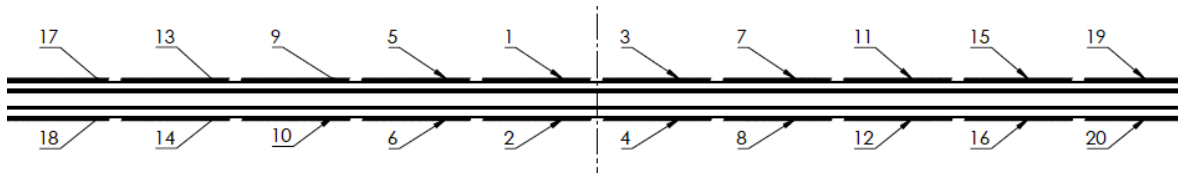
Verworfenne Schweißfolge 1 für Trapezlängssteife (von innen nach außen alternierend geschweißt)
